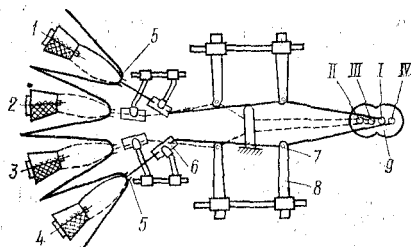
Схема заправки нитей с бобин для четырехуточного прибора станка СТБ4-330
